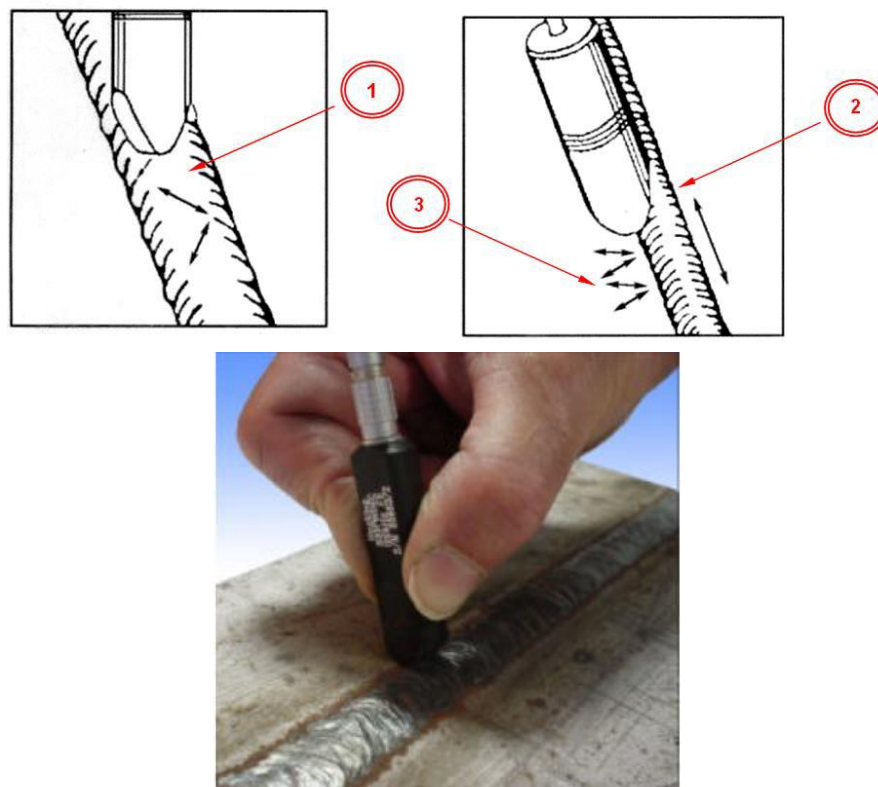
Вихретоковый контроль стыкового сварного соединения
